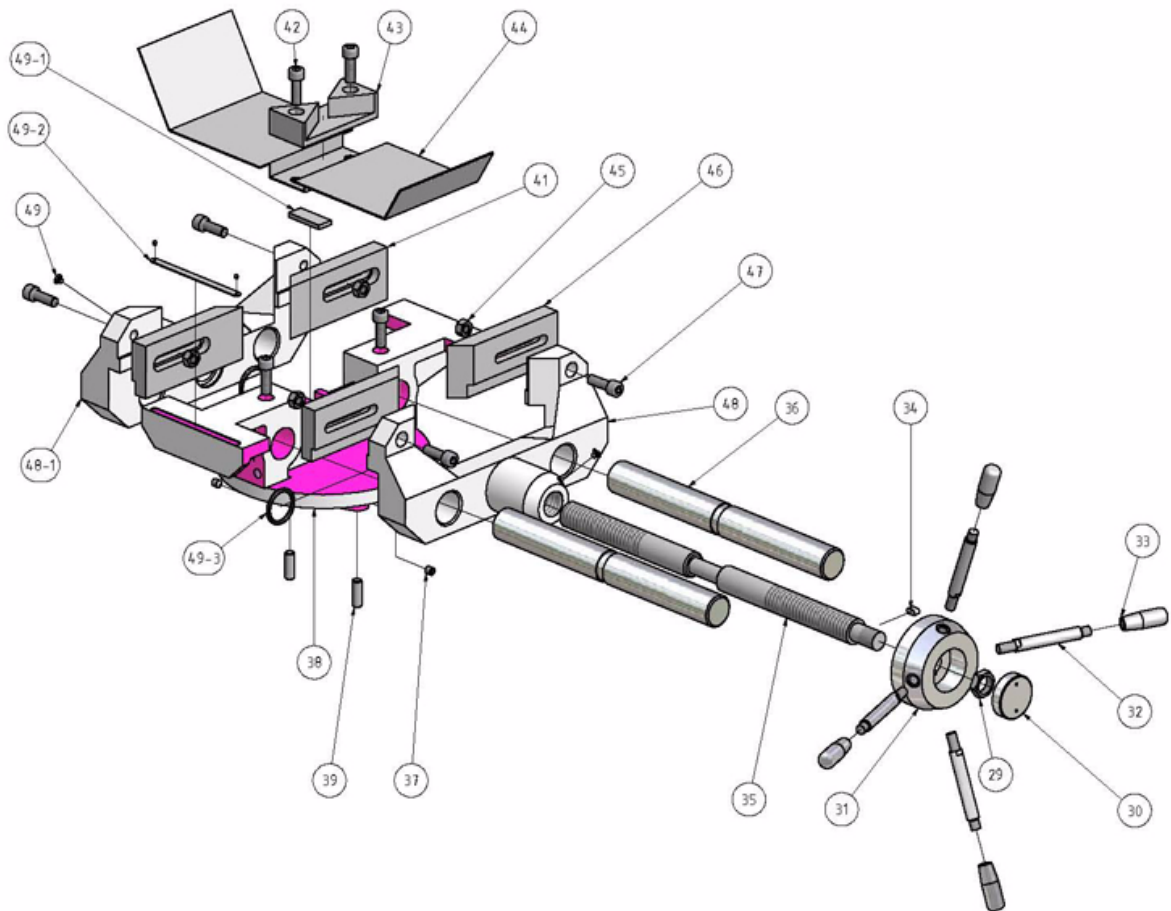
Schnellspannschraubstock - Machine vice - CS275/ CS315
